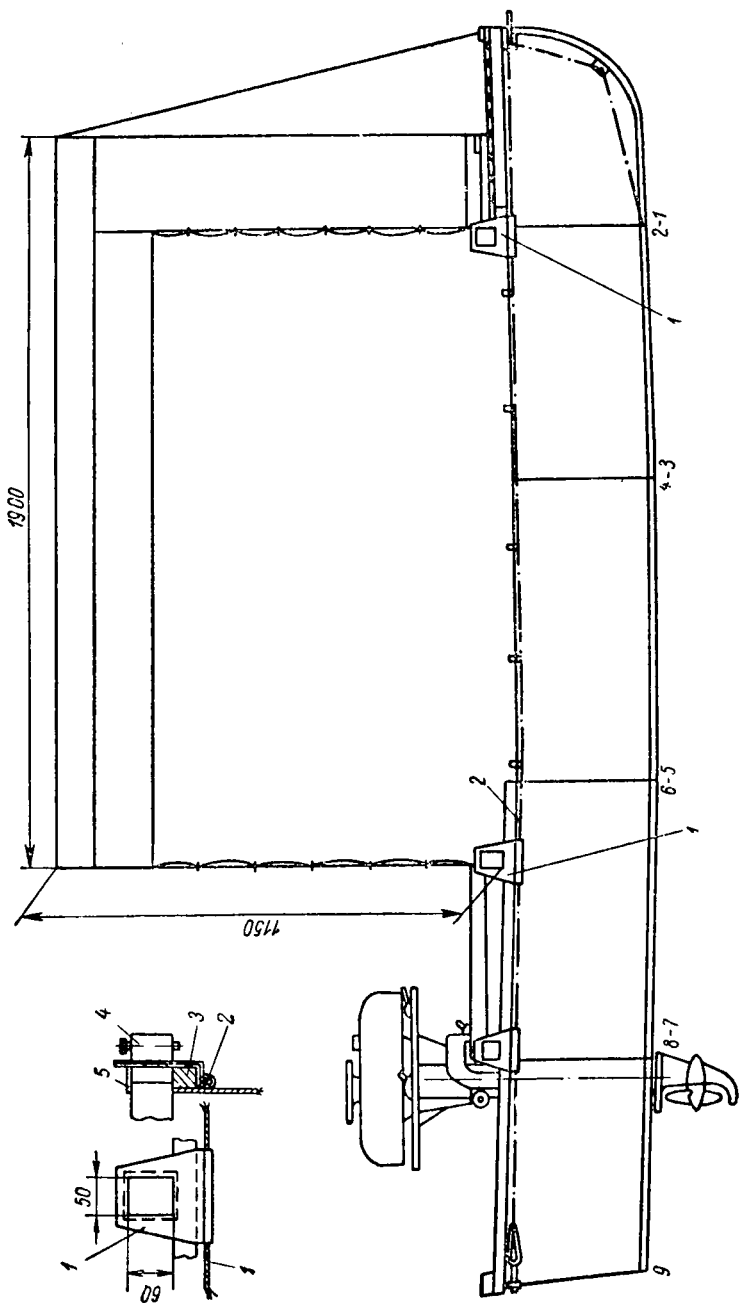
Разборная двухкорпусная дача «Ладoga» ДБ (вид сбоку).
